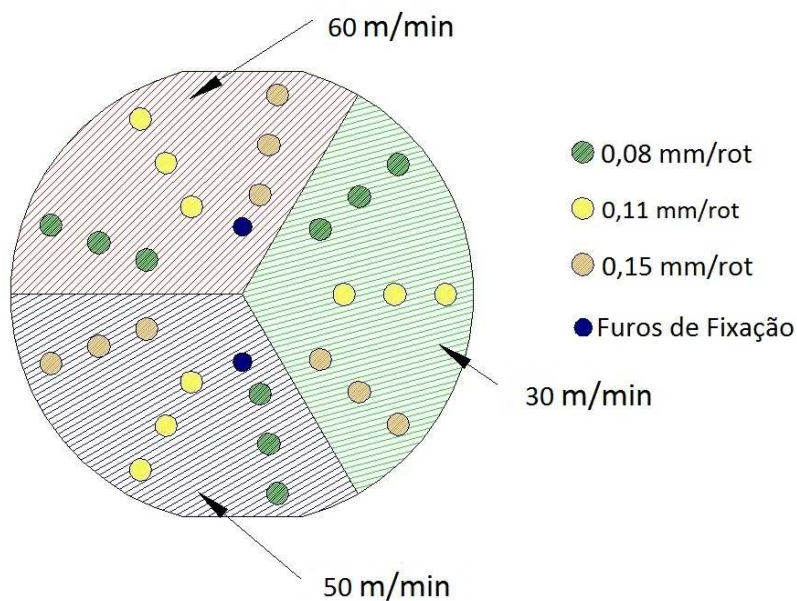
Layout da amostra no ensaio de Alargamento
